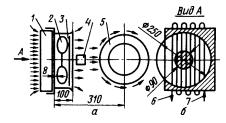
Схема холодильного агрегата BCp400 1 (вид сверху):
